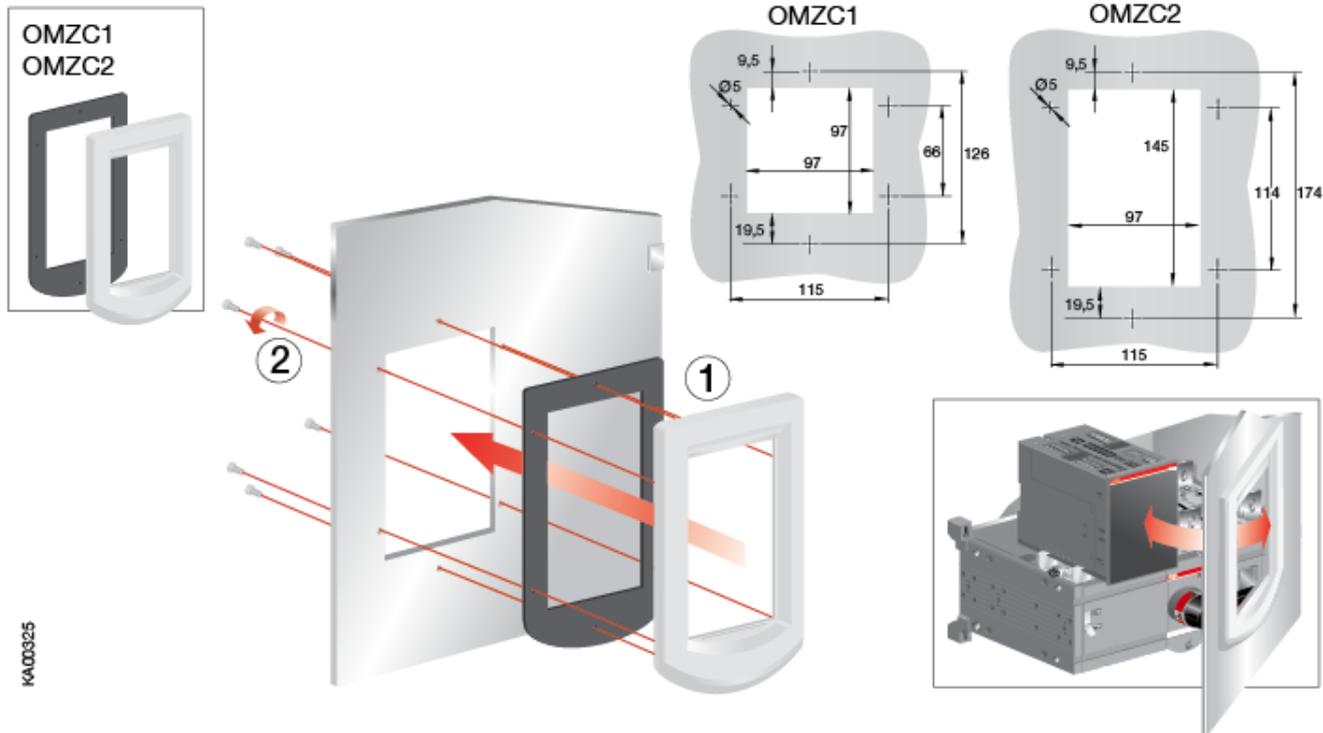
Прорезь в двери и установка защитной пластины OMZC_, при установке блока автоматического управления OMD_ на корпусе реверсивного выключателя нагрузки или на DIN-рейке
